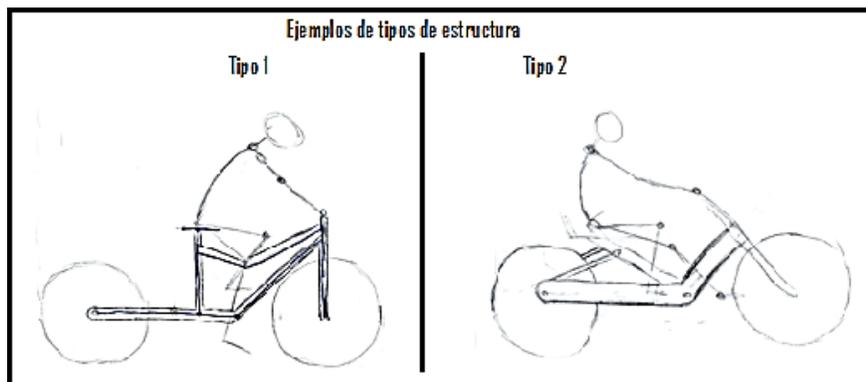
Ejemplos de tipos de estructuras planteadas
